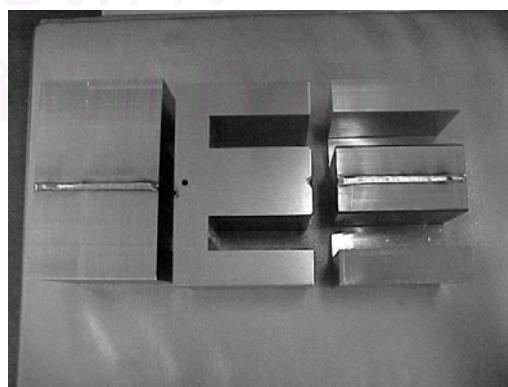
เครื่อง I-Block welding
